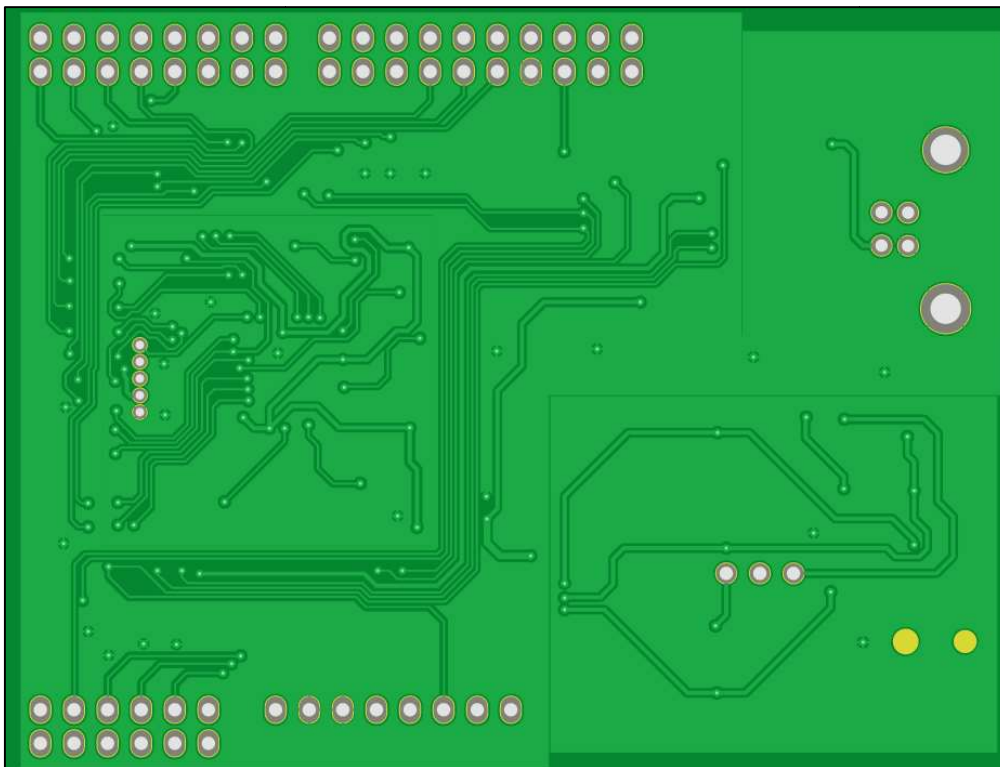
Vista previa del módulo PCB en PCB Visualizer: cara BOTTOM
